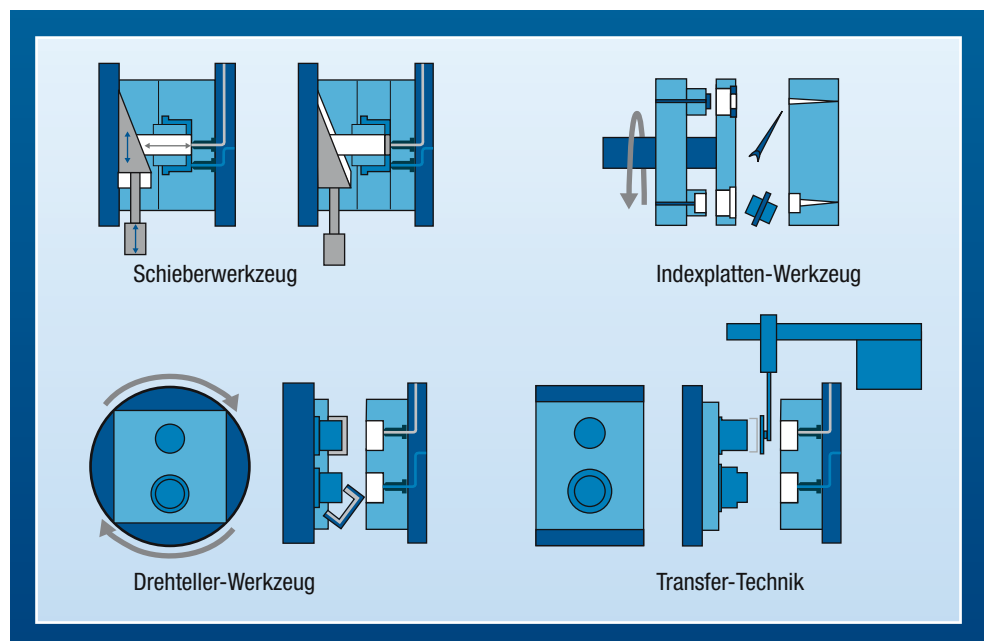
Werkzeugtechniken beim Mehrkomponenten-Spritzgießen
